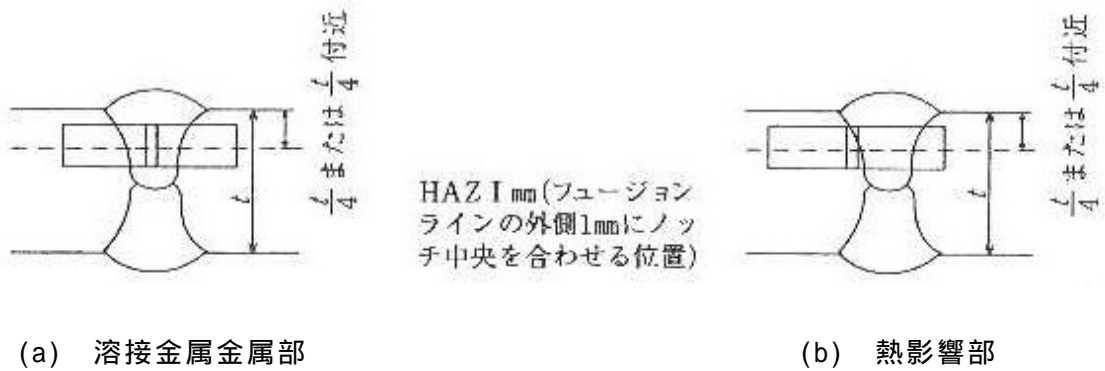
衝撃試験片（開先溶接試験片の採取位置）
